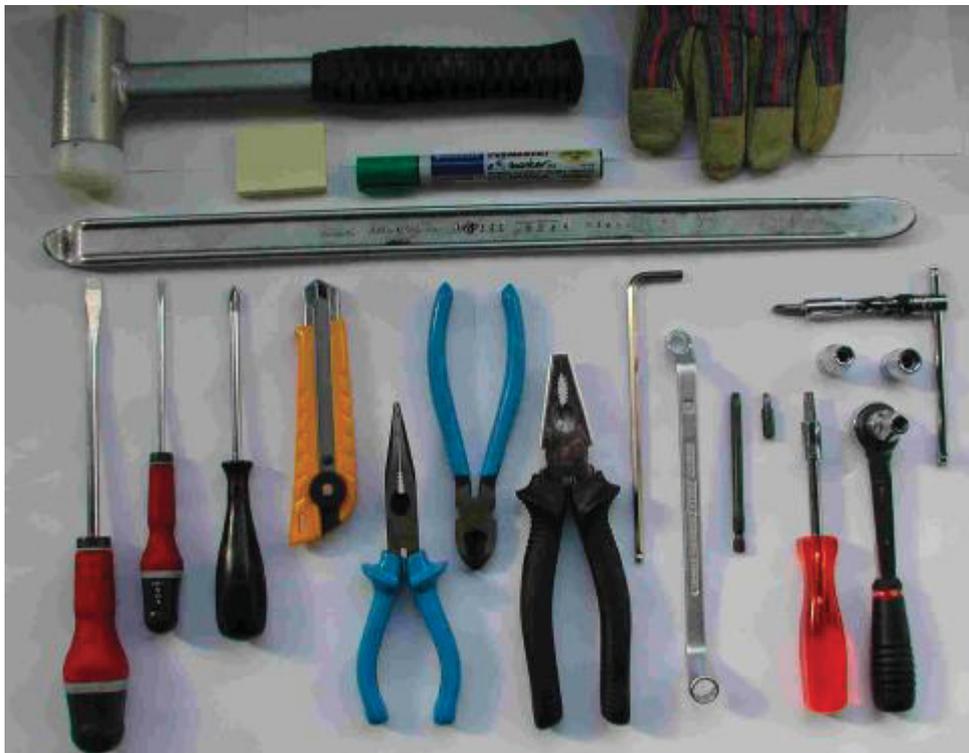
Verwendetes Werkzeug bei der Türdemontage
